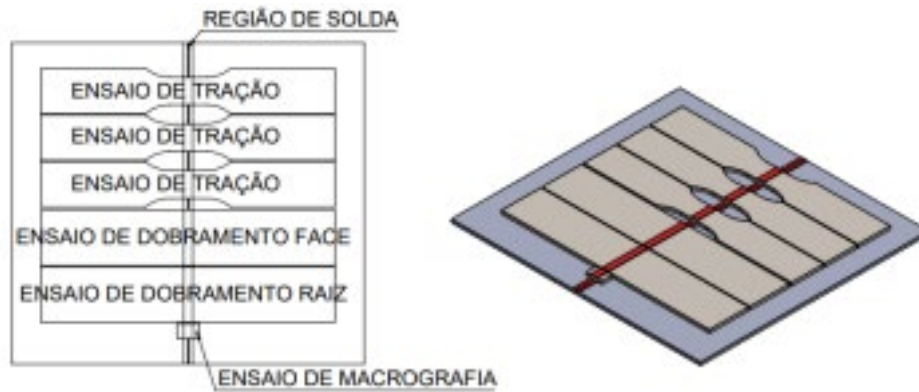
Disposição dos corpos de prova nos conjuntos soldados para extração.
